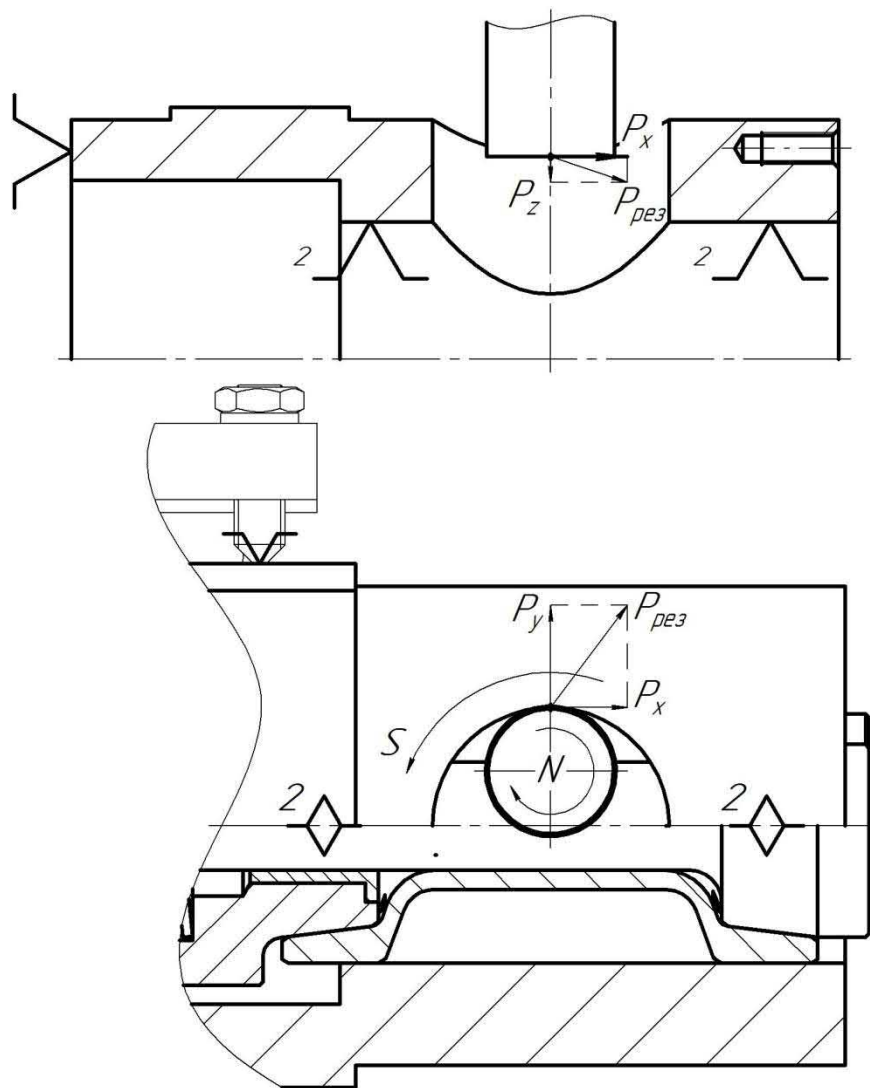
схема установки заготовки с силами, действующими в процессе обработки
